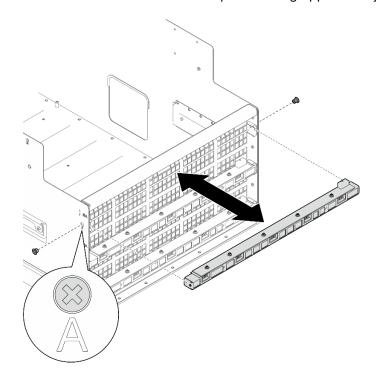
Entfernen der hinteren Lüfterplatinenbaugruppe
